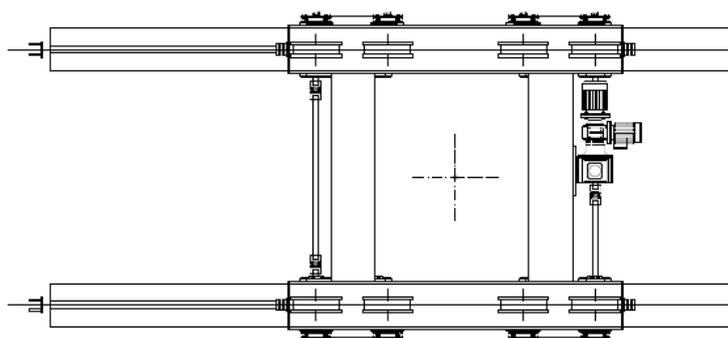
Carrello di trasferimento DW007 - vista in pianta
